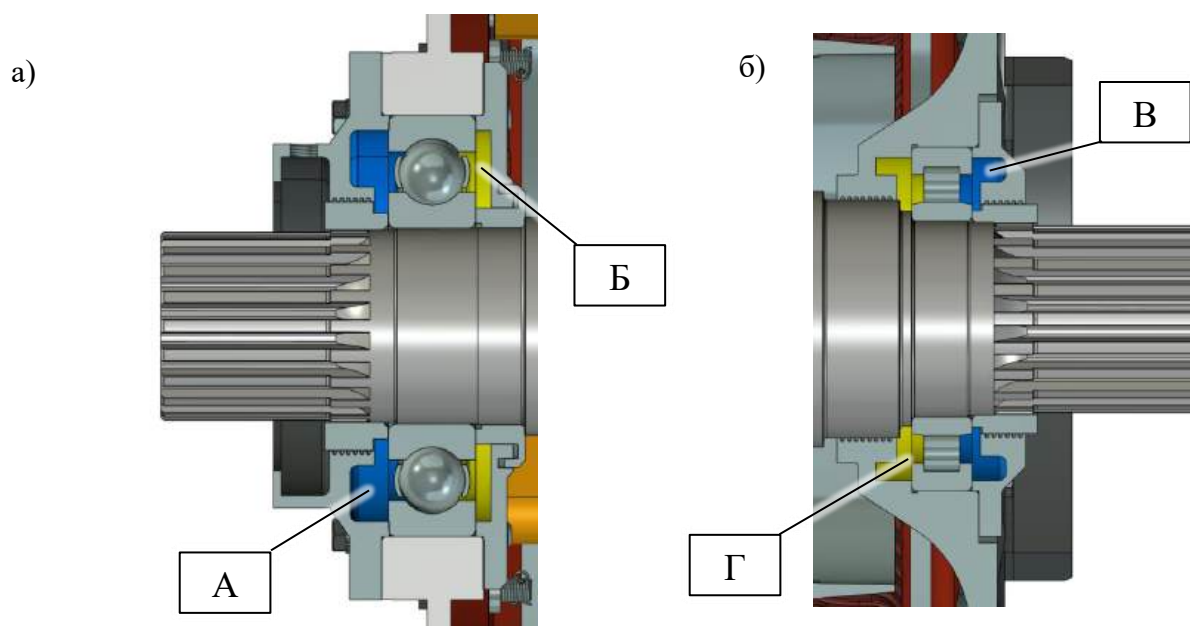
Пополнение смазки в подшипниковых узлах:
